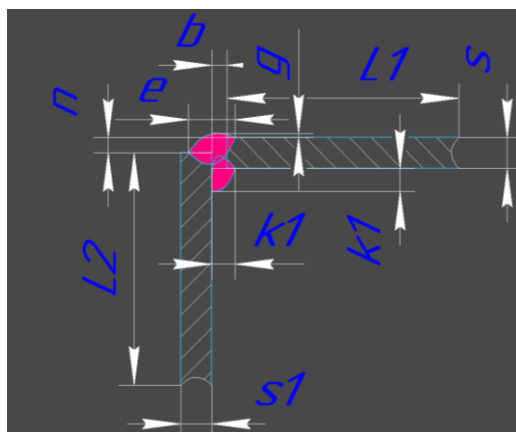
Загальний вигляд кутового зварного з'єднання У5
